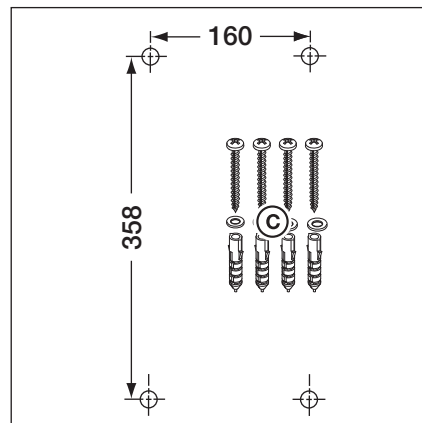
Схема расположения отверстий для крепления, необходимые детали для монтажа
